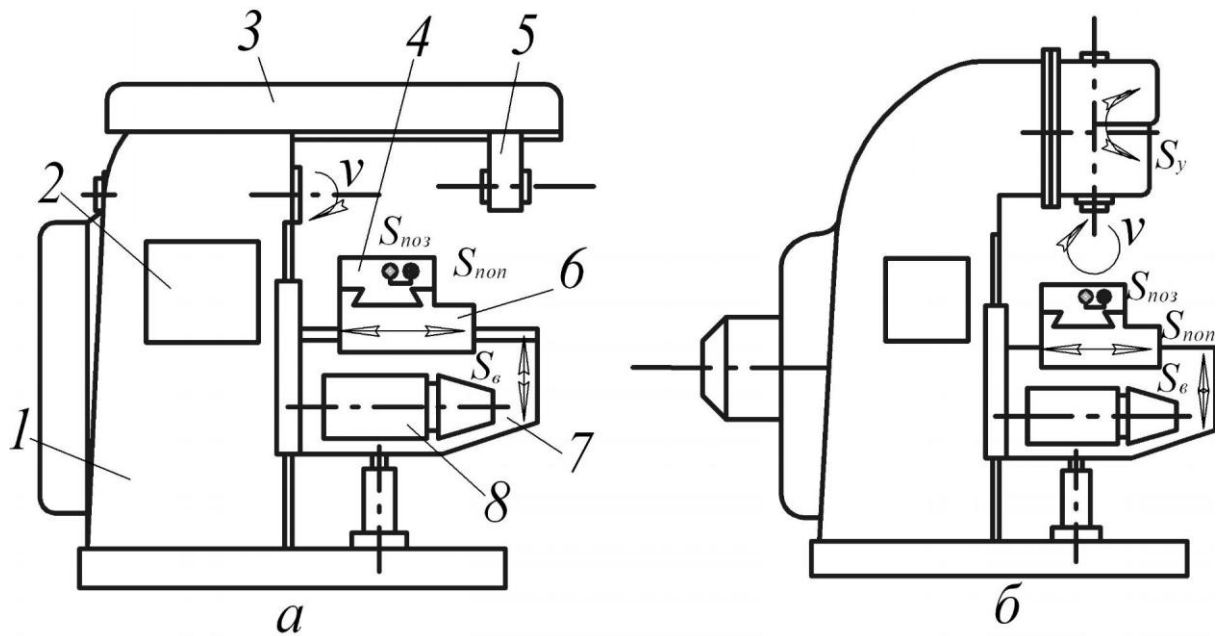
Консольні горизонтально-фрезерний (а) і вертикально-фрезерний (б) верстати
